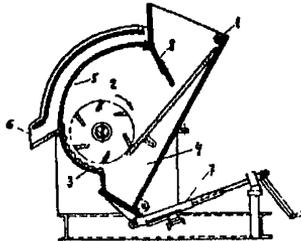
Фрезерно-струйная мельница ФСМ-3:
